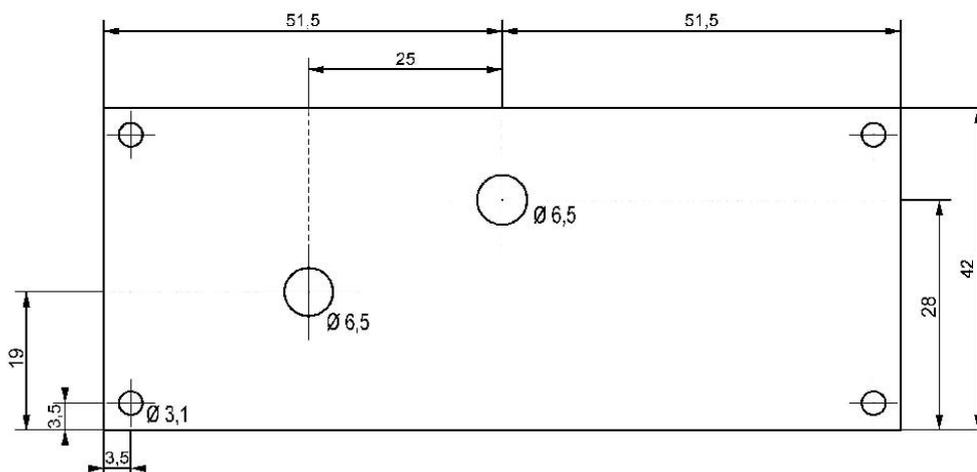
Bohrplan für die Gehäuse-Frontplatte
